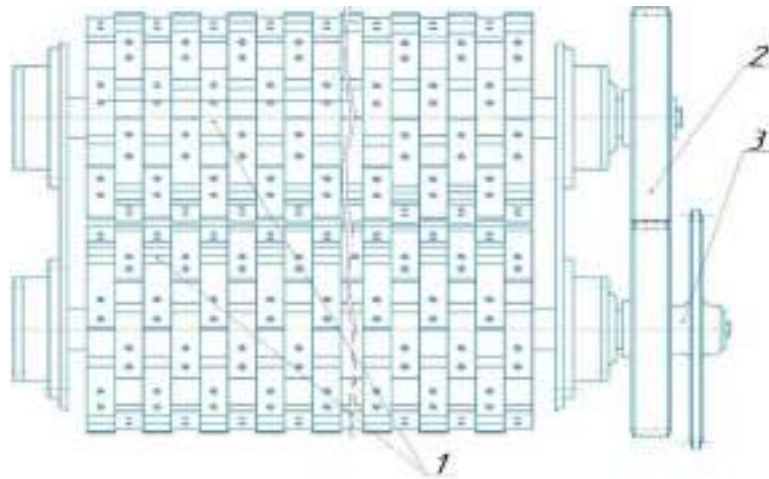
Подрібнювач: 1 – Подрібнюючі вали; 2 – зубчаста передача; 3 – зірочка приводу валів
